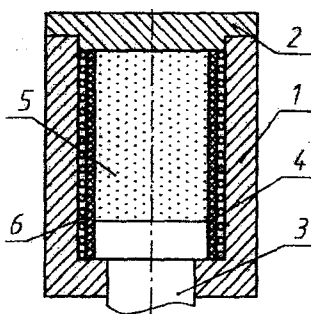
Метод сухого мешка: 1 – обойма гидростата; 2 – верхняя крышка; 3 – выталкиватель порошковой заготовки; 4 – резиновая оболочка; 5 – порошок в засыпанном состоянии в начале и в виде уплотненной заготовки в конце; 6 – элементы упругой подвески резиновой оболочки внутри корпуса гидростата
